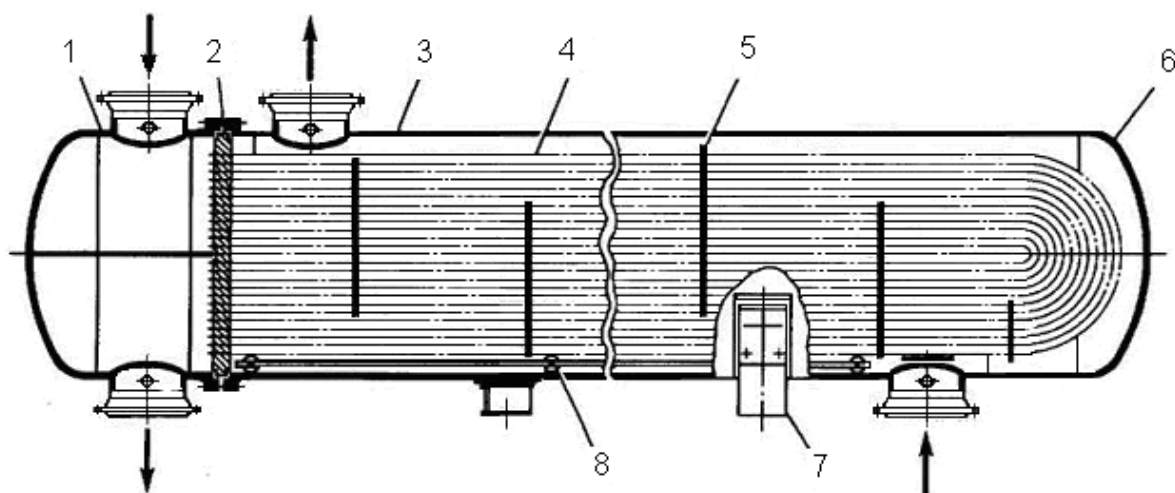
Кожухотрубчастий теплообмінник з U-подібними теплообмінними трубами: 1-розподільна камера; 2-трубні грати; 3-кожух; 4-теплообмінна труба; 5-поперечна перегородка; 6 - кришка кожуха; 7-опора; 8-коткова опора трубного пучка
